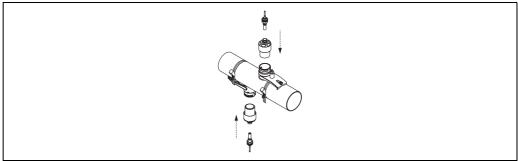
Montaggio del sensore e collegamento del cavo di collegamento
